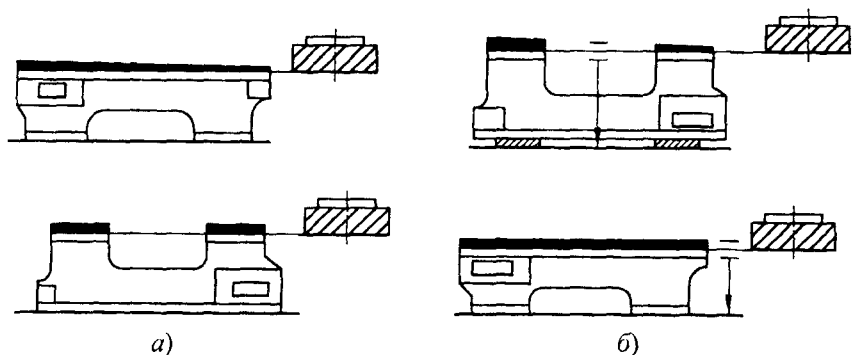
Схема последовательности обработки станины токарного станка на первых операциях:
